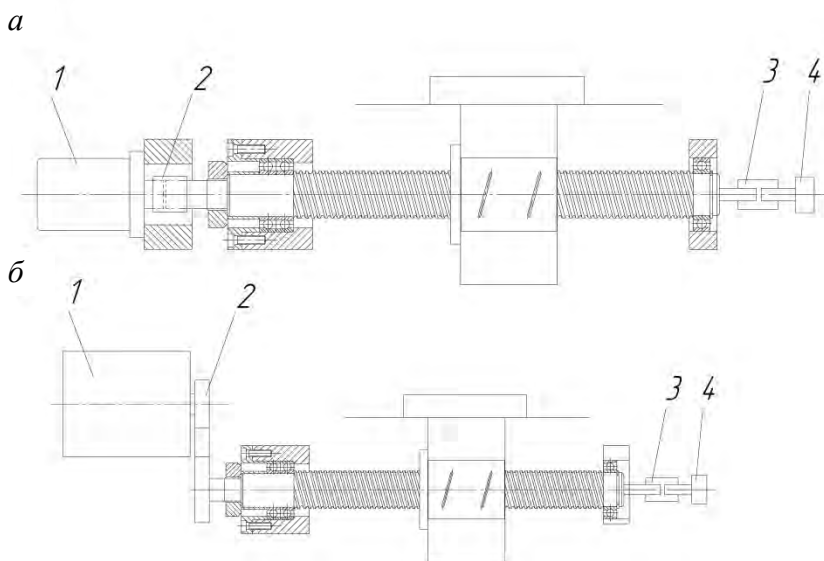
Схемы исполнительного механизма привода подачи с приводным винтом
